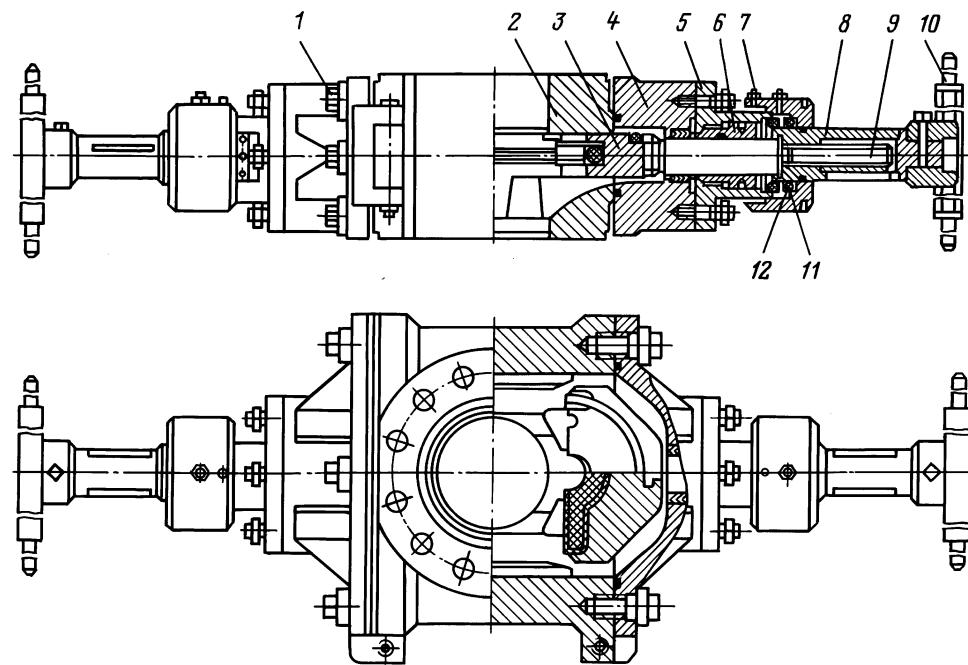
Малогабаритный превентор для ремонта скважин ППР
